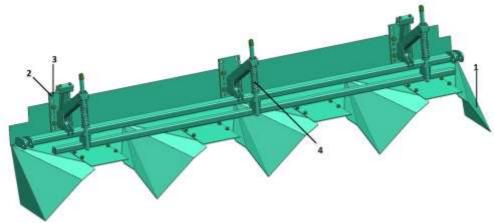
Гребнеобразователь 1 – щит; 2 – скоба; 3 – стойка; 4 – пружина.
